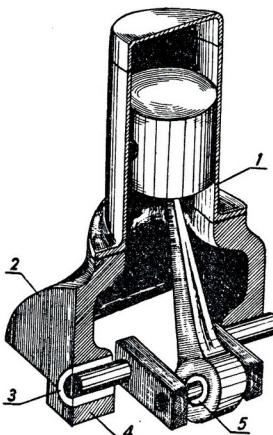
Разрез двигателя: 1 — цилиндр, 2 — корпус двигателя, 3 — главный подшипник, 4 — крышка главного подшипника.
